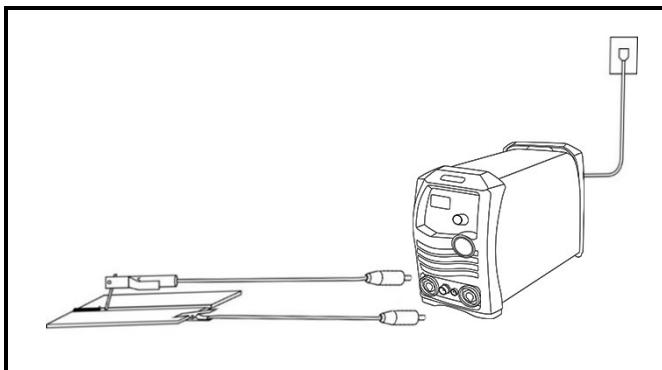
Подключение при ручной дуговой сварке (ММА, обратная полярность).
